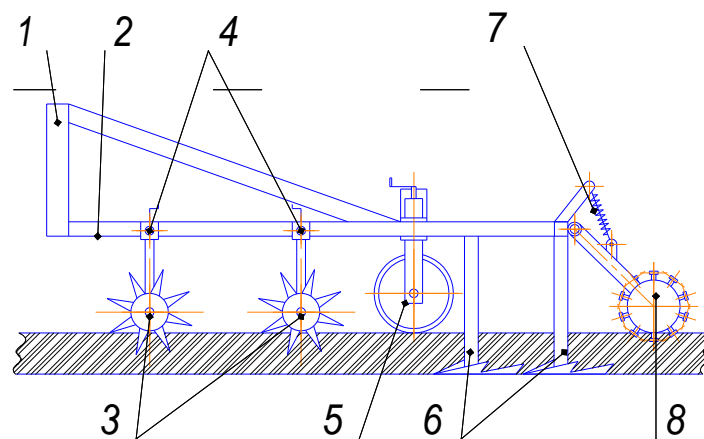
Ґрунтообробний агрегат для мілкої мульчуючої обробки ґрунту: 1 – навісний пристрій; 2 – рама; 3 – батареї ножових дисків; 4 – механізми регулювання глибини обробки і кута атаки ножових дисків; 5 – опорно-регульовальні колеса; 6 – плоскоріжучі лапи з розпушувальними елементами лемешів; 7 – механізм довантажування катка; 8 – каток з штифтовими елементами
